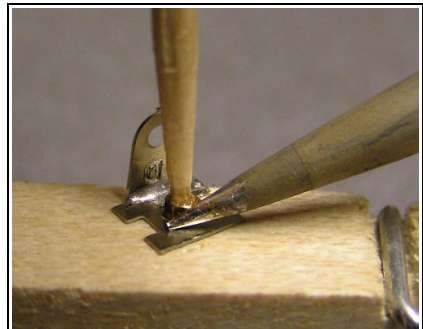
Mutter fest aufdrücken um zu verhindern, dass Zinn in die Gewindegänge gelangt. Mutter verlöten.
